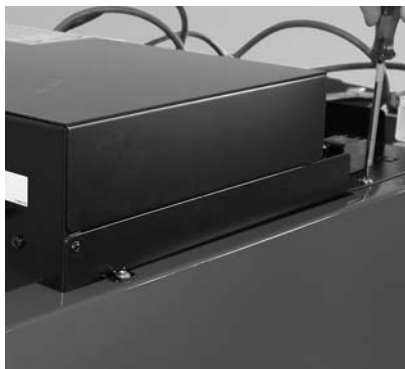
LogWIN 180-300 Seitenwände mit Schaltfeld 4 x verschrauben
